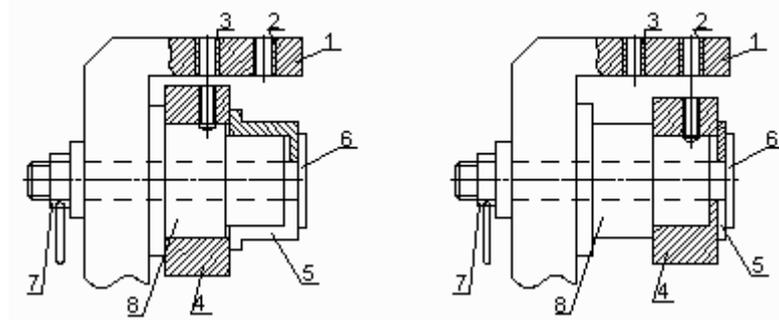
Кондуктор для сверления отверстий в деталях двух типоразмеров.
